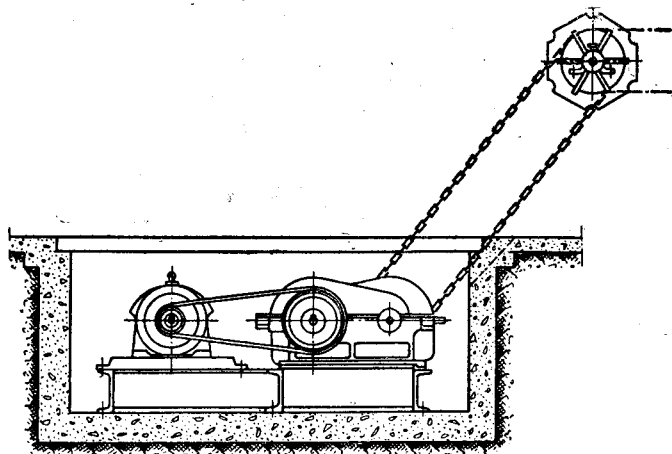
Привод конвейера с двумя цилиндрическими редукторами.
